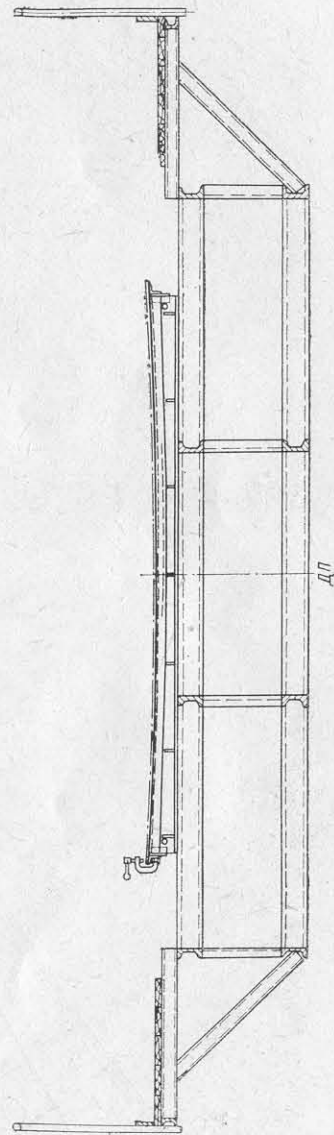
Постель для сборки и сварки палубы носового блока.
